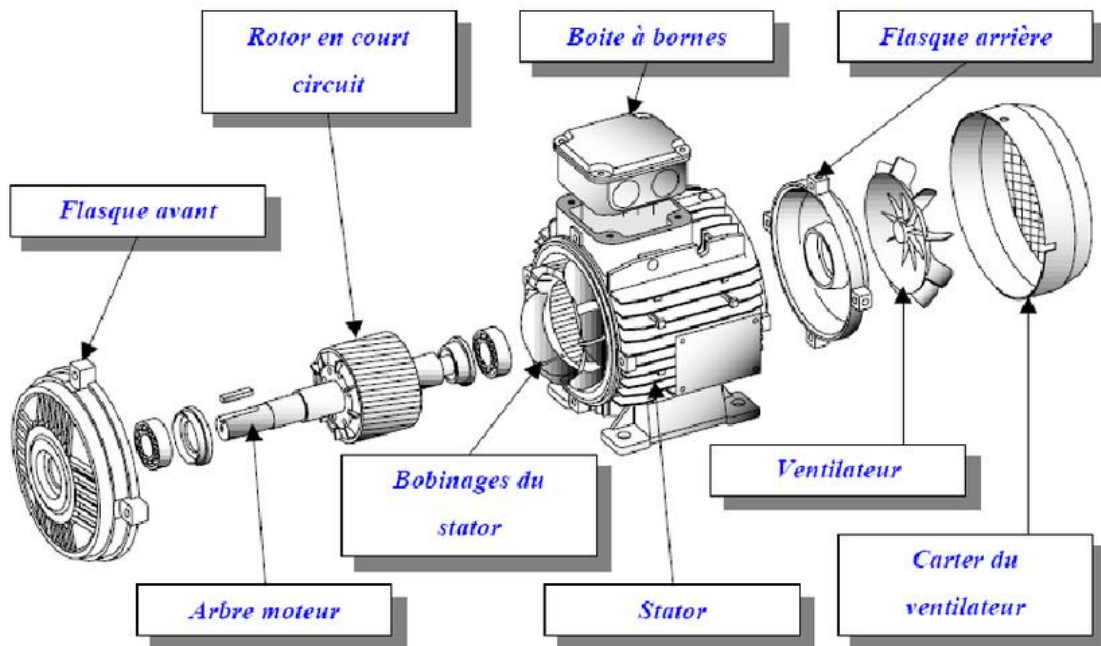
Forme éclatée d'un moteur asynchrone (moteur électrique).
